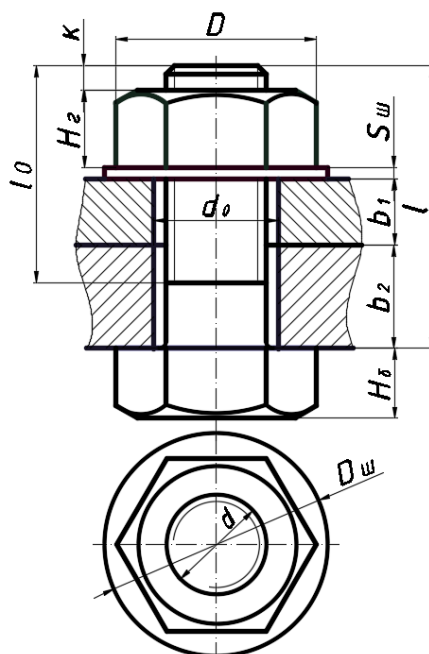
Образец конструктивного изображения болтового соединения.
